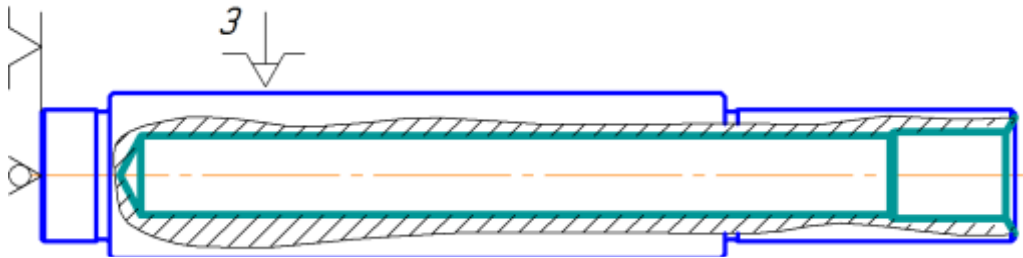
Схема базування при обробці вала на операції 035
